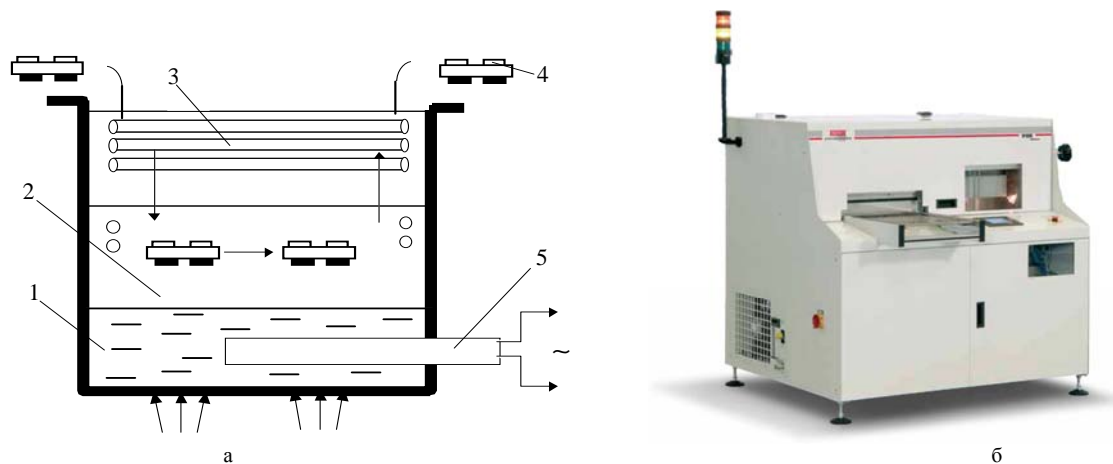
Схема (а) и внешний вид (б) установки пайки в паровой фазе камерного типа
